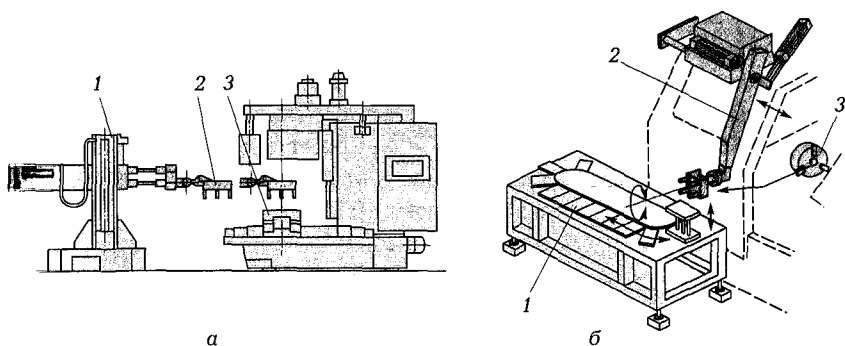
Схемы автоматизации загрузки-разгрузки заготовок и деталей на станках с ЧПУ:
